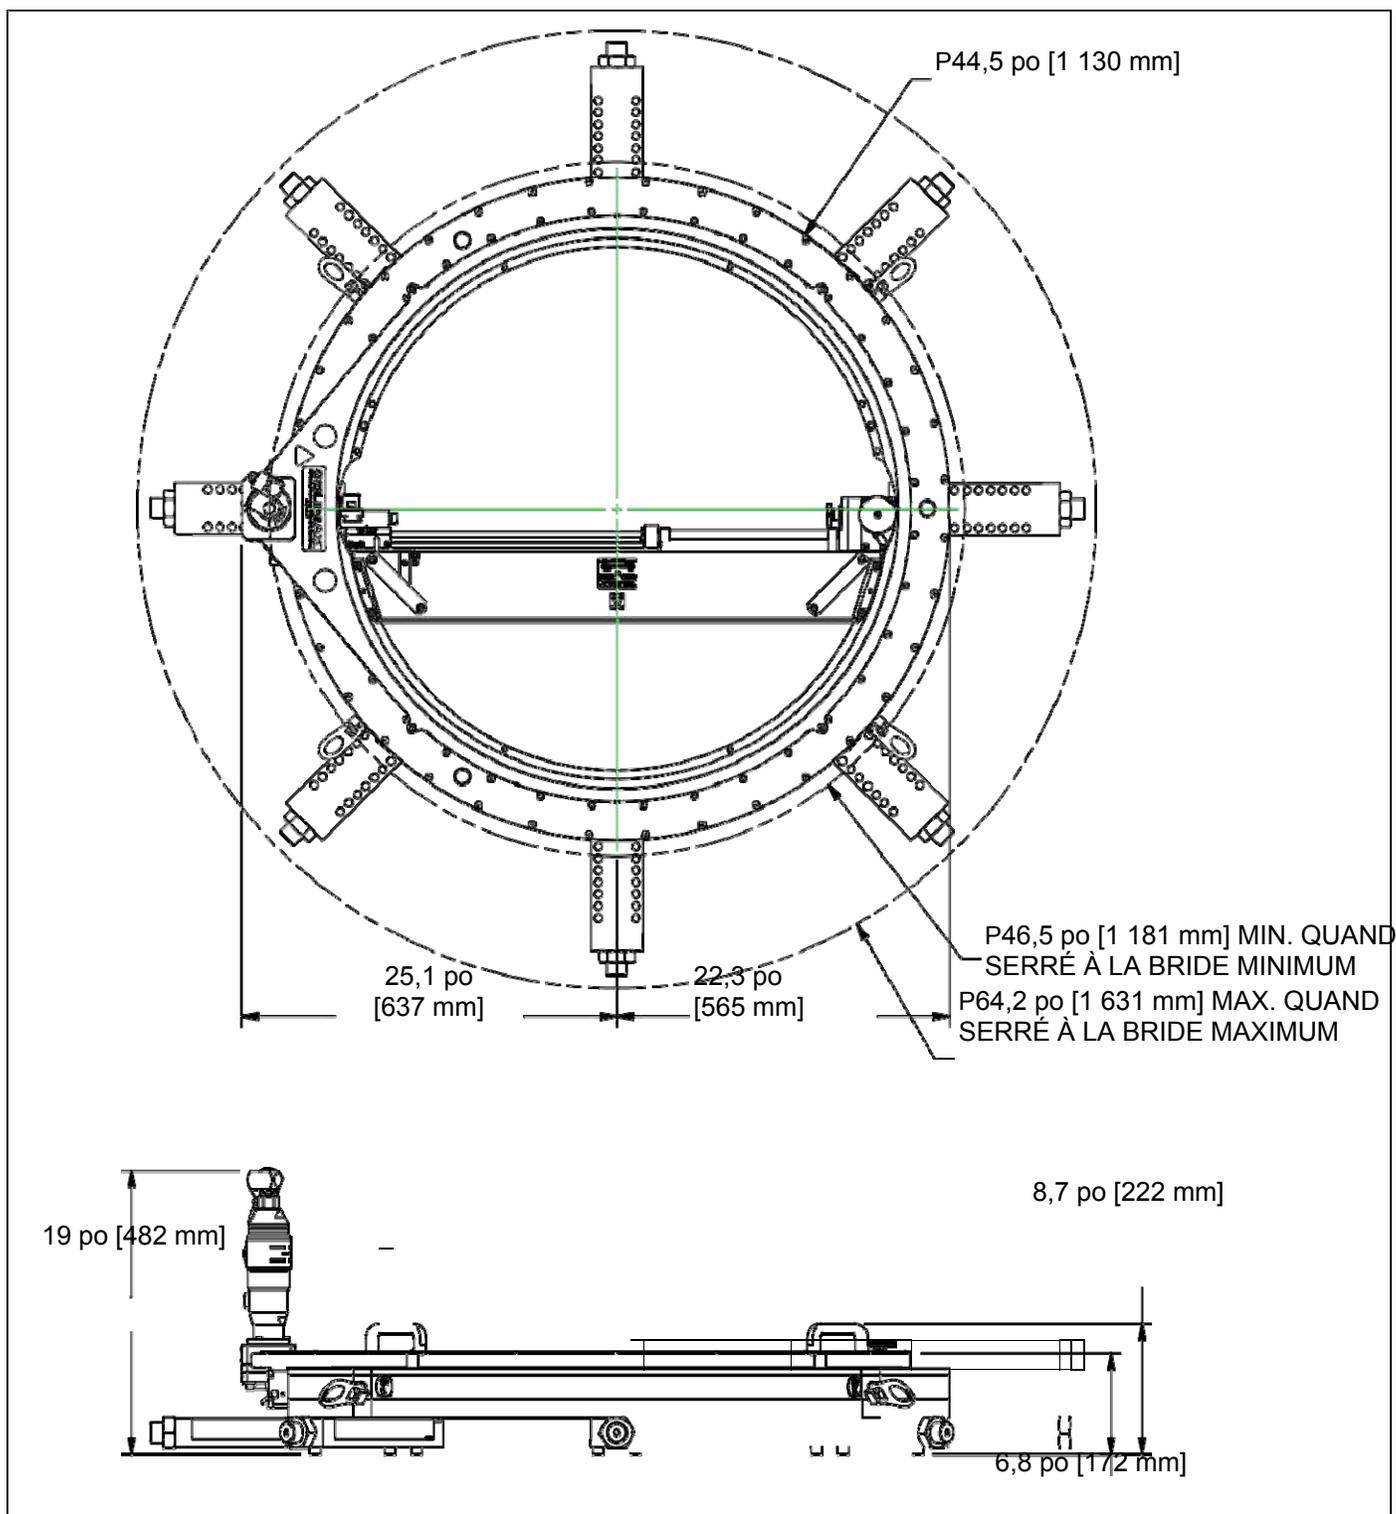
DIMENSIONS DE LA MACHINE FF3600
